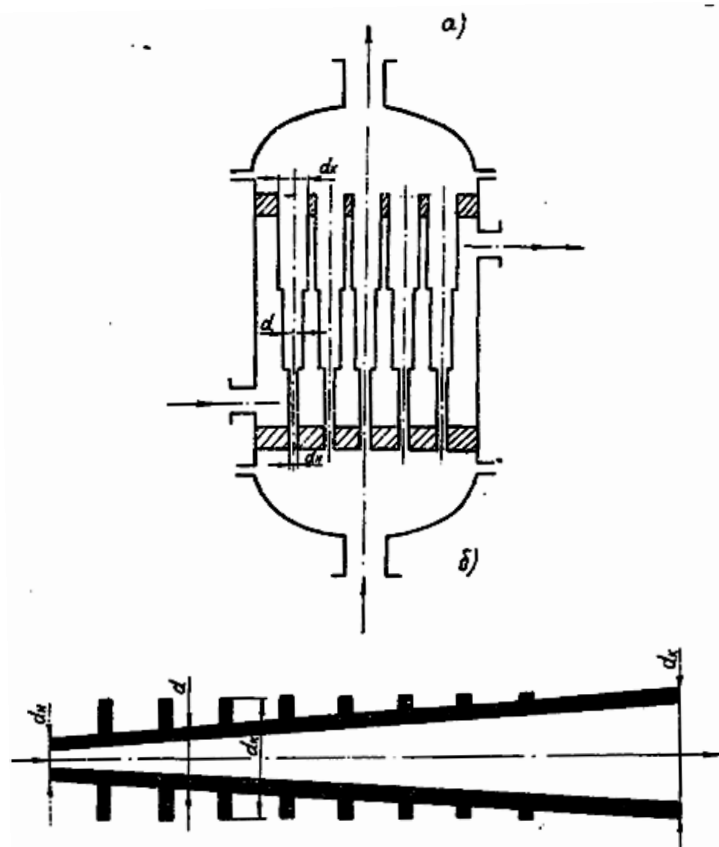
Общий вид кожухотрубного реактора с секционными трубами (а) и конической оребренной снаружи трубы (б)
